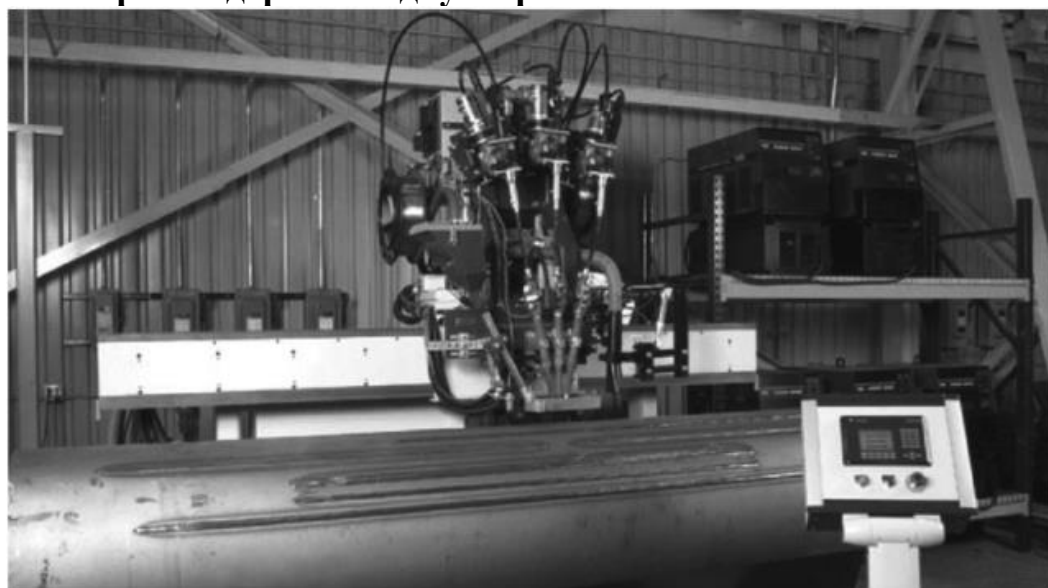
Многодуговой автомат для сварки продольных швов труб
